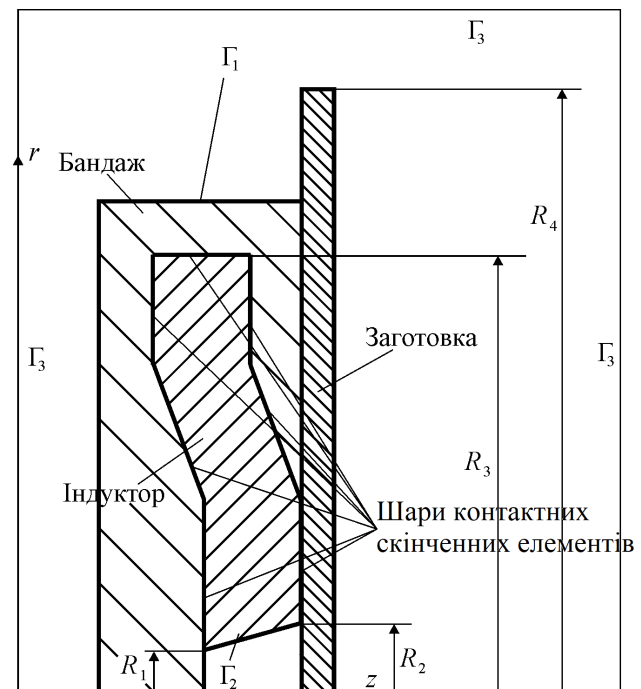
Розрахункова схема складеного одновиткового індуктора та плоскої заготовки
